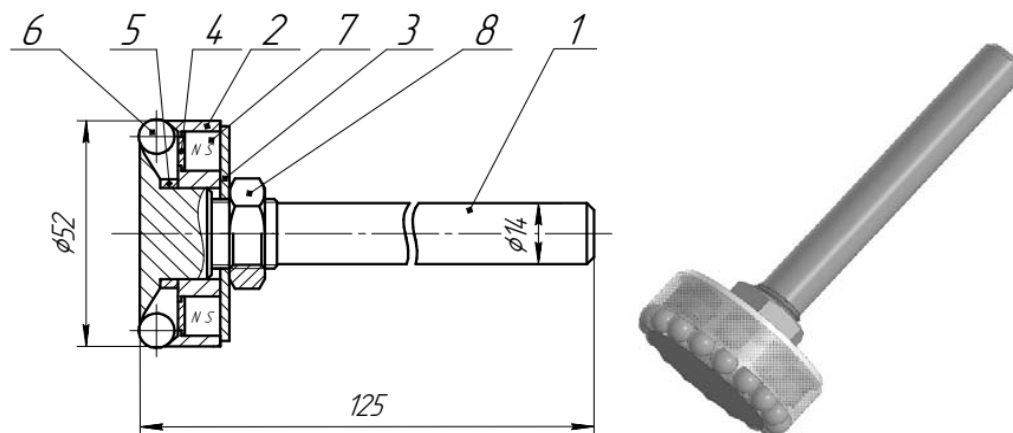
Конструкция инструмента для магнитно-динамического упрочнения валов
